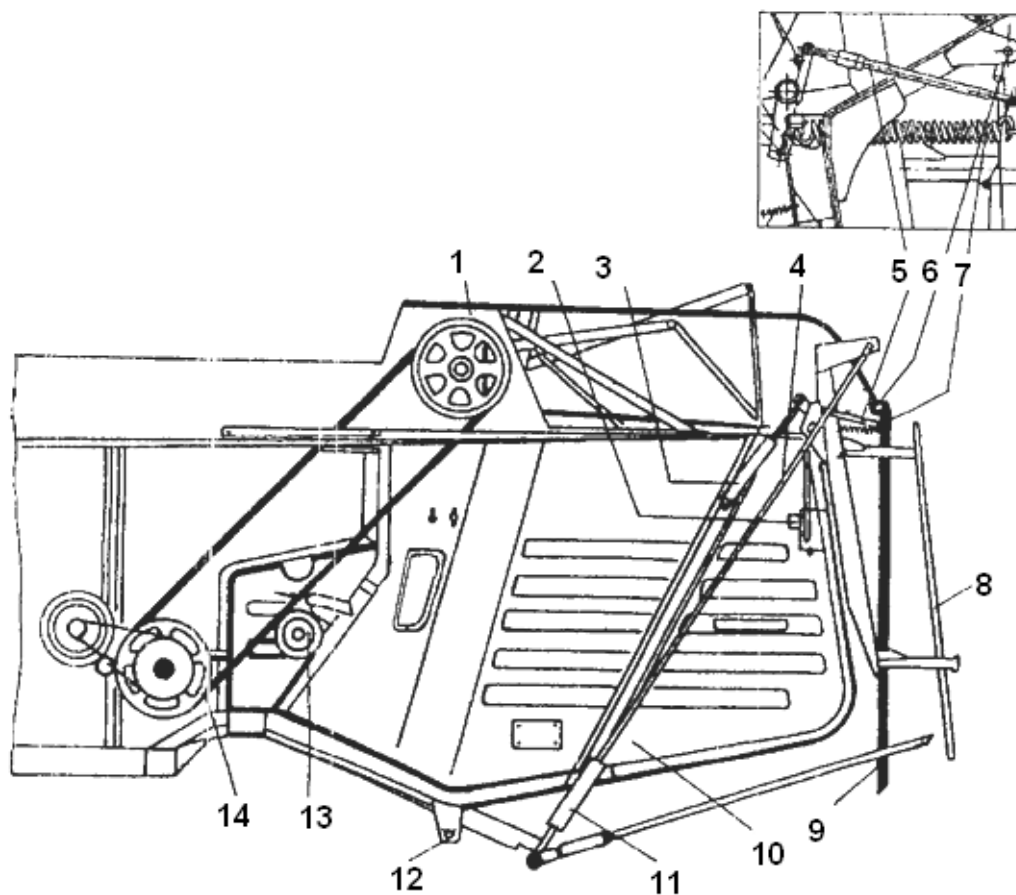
Копнитель навесной гидрофицированный (вид слева): 1 – капот; 2 – включатель; 3 – гидроцилиндр; 4, 5 – тяги; 6 – ось; 7 – пружина; 8 – клапан; 9 – сигнализатор сброса копны; 10 – боковина; 11 – гайка стяжная; 12 – ось подвески днища; 13 – шкив натяжной; 14 – ремень приводной
